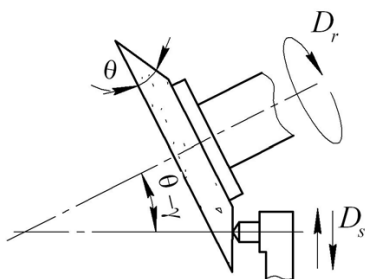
Установка шпинделя шлифовального круга при правке конической поверхности круга тарельчатой формы
